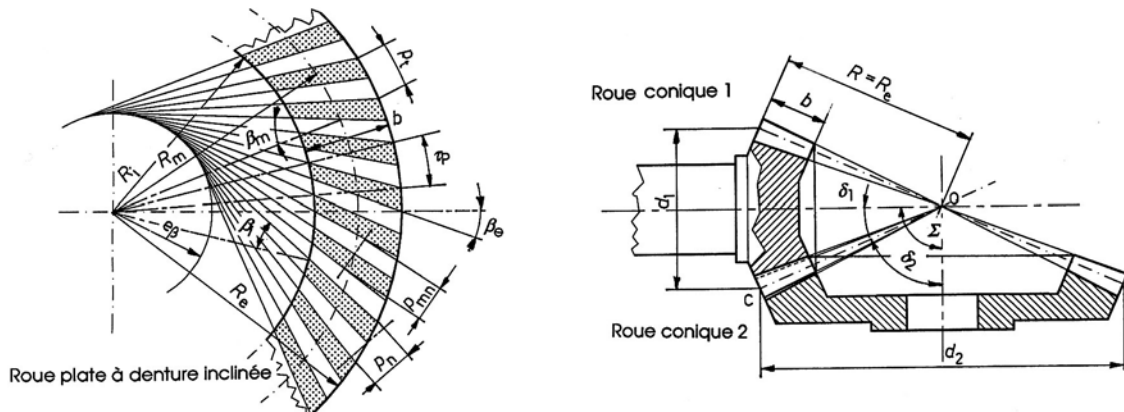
Définitions des rayons, des angles et des pas sur la roue plate Engrenage conique
